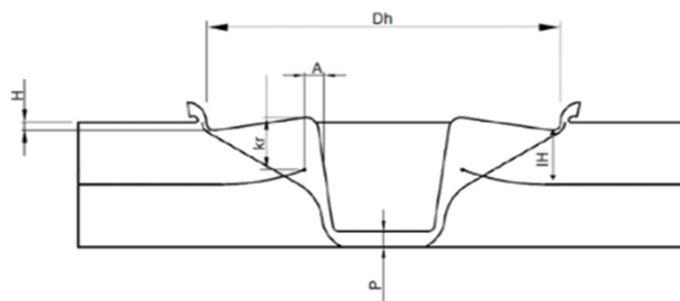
Partes de la soldadura de punto por fricción- agitación
